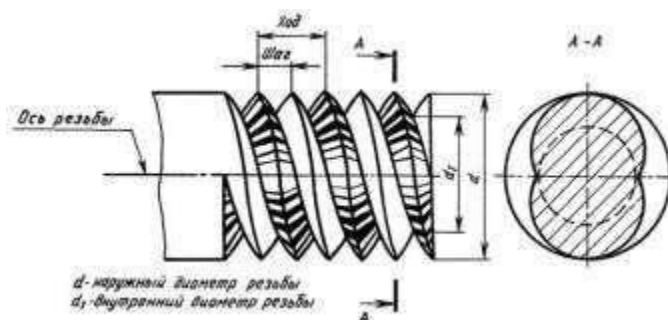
Резьба цилиндрическая двух заходная
